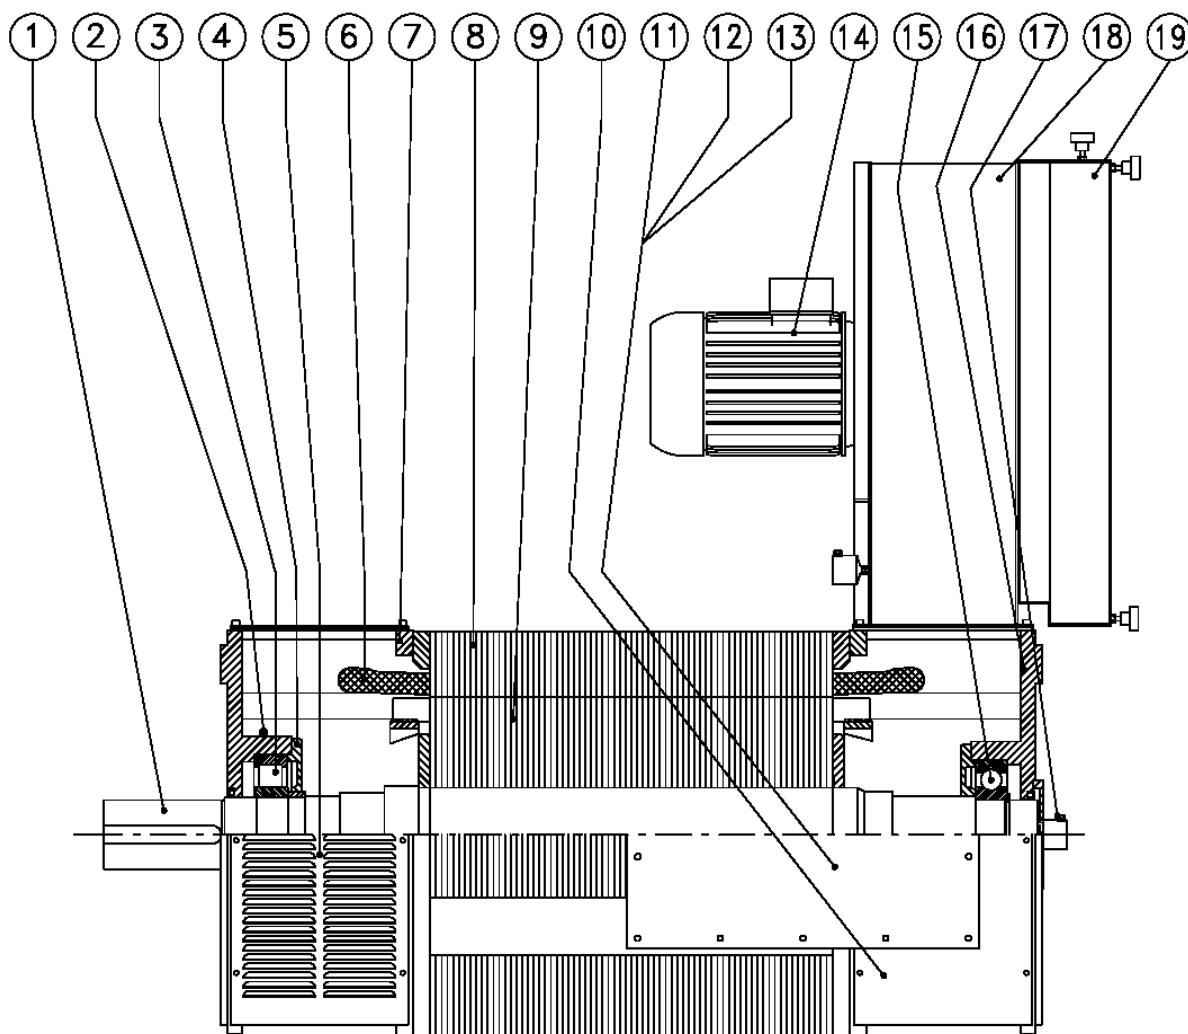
Disegno dimostrativo d'assieme motori SQ180-225
